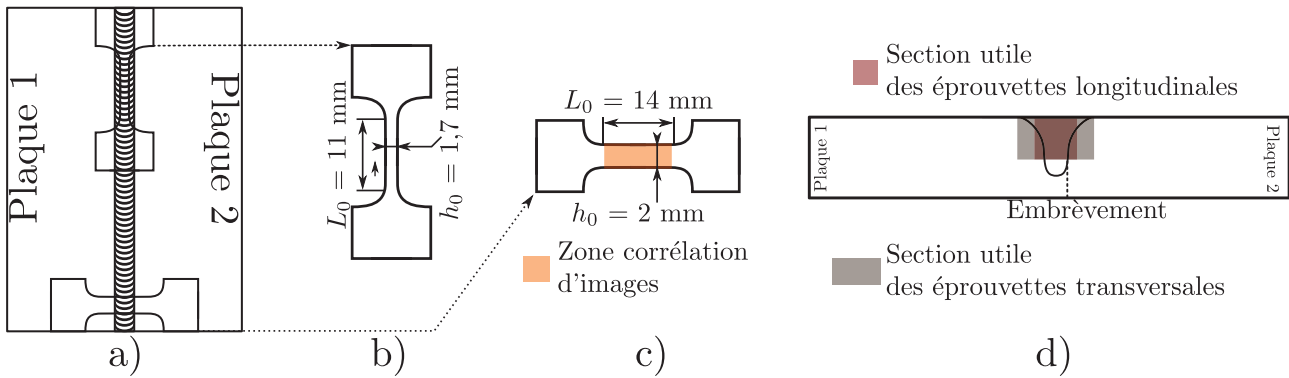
Géométrie des éprouvettes utilisées pour caractériser le comportement mécanique des liaisons soudées, a) zone de prélèvement, b) géométrie des éprouvettes longitudinales, c) géométrie des éprouvettes transversales et d) section utile des éprouvettes longitudinales et transversales
